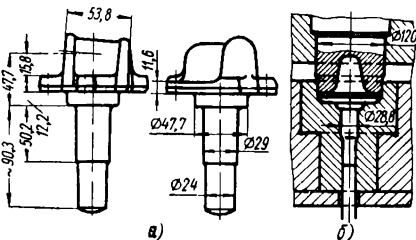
Поковка поворотного кулака мотоколяски: а — поковка; б — схема штампа первого перехода
